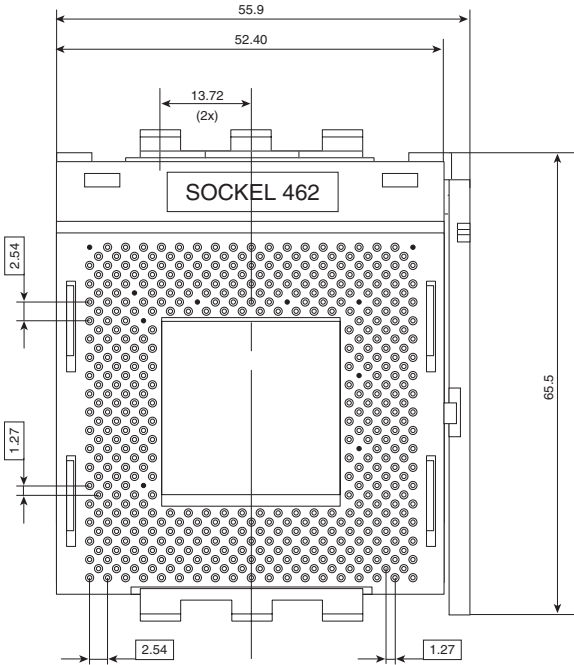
Das Layout von Sockel A (Sockel 462)
